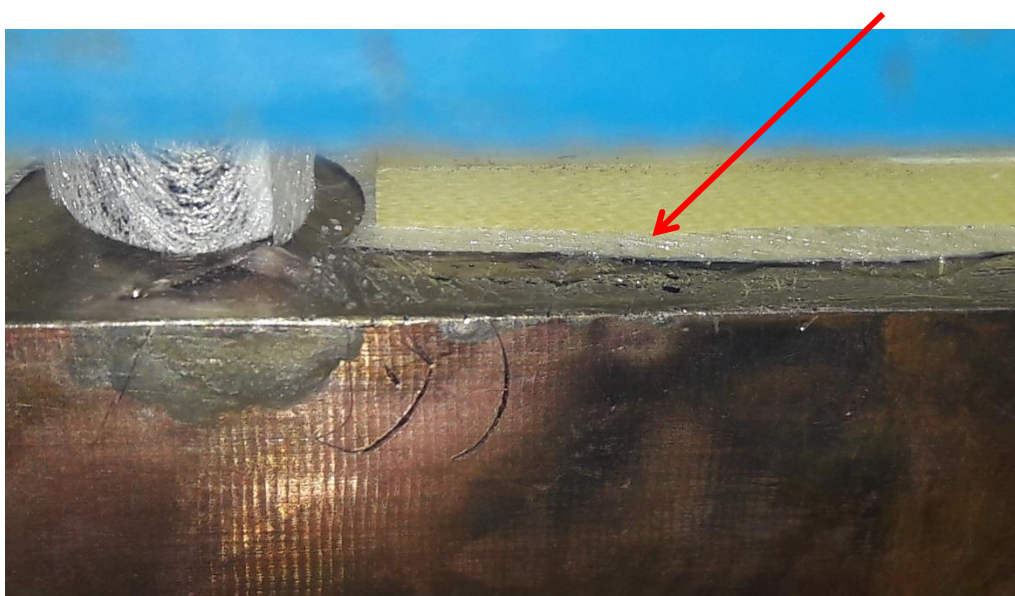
Zoom nas trincas da solda lado direito
